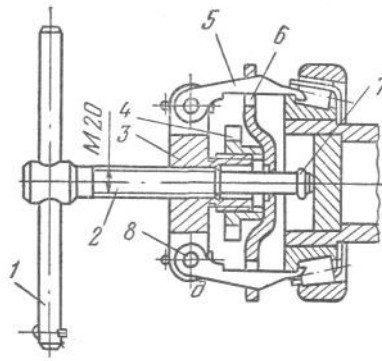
Знімач зовнішнього підшипника маточини веденої шестерні кінцевої передачі: 1- вороток; 2- силовий гвинт; 3- траверса; 4- наживна гайка; 5- захват; 6- шайба; 7- кільце; 8- пальці.
